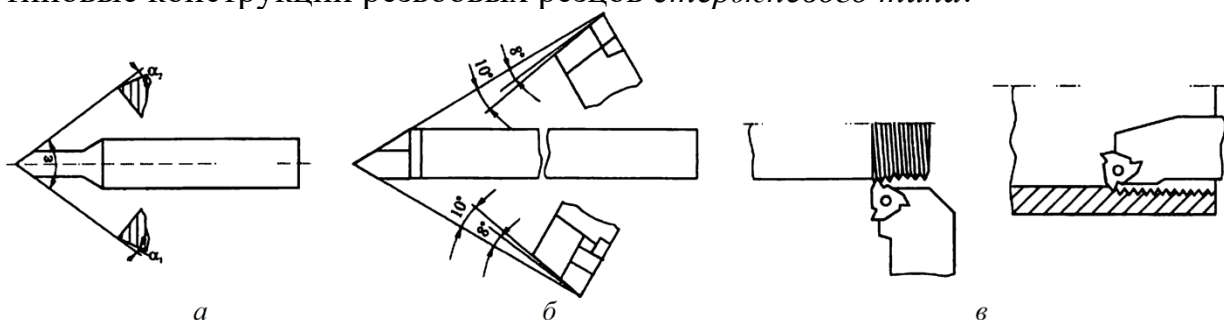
Типы стержневых резьбовых резцов: *а* – цельный из быстрорежущей стали; *б* – с напаянной твердосплавной пластиной; *в* – с механическим креплением твердосплавной пластины
